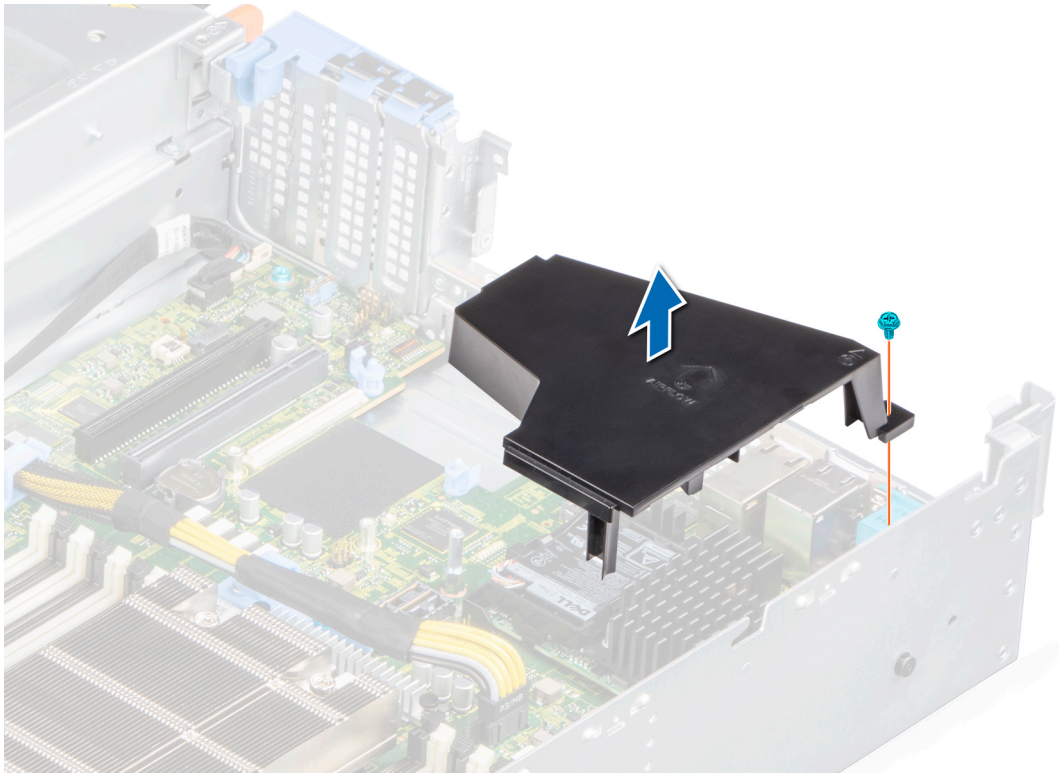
Entfernen des Kühlgehäuses der Mini-PERC-Karte
